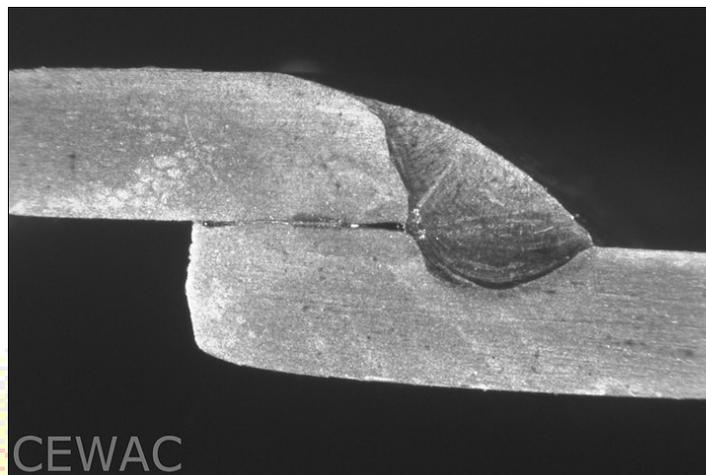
soudure HLW par recouvrement d'inox 316L (1,5 mm) à 3 m/min
